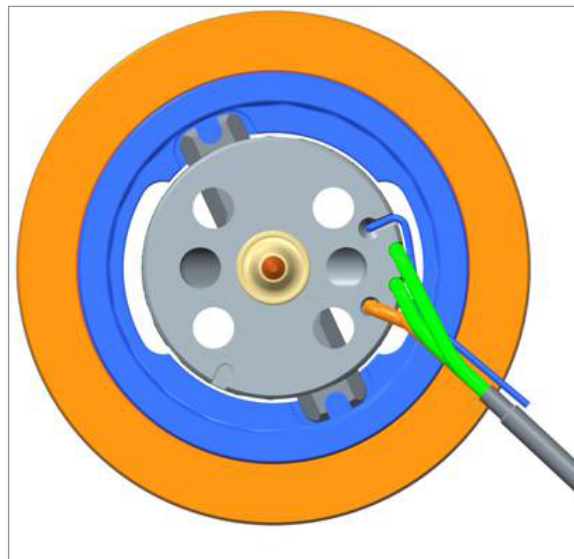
Draufsicht auf die eingesezte Kolbenbaugruppe
